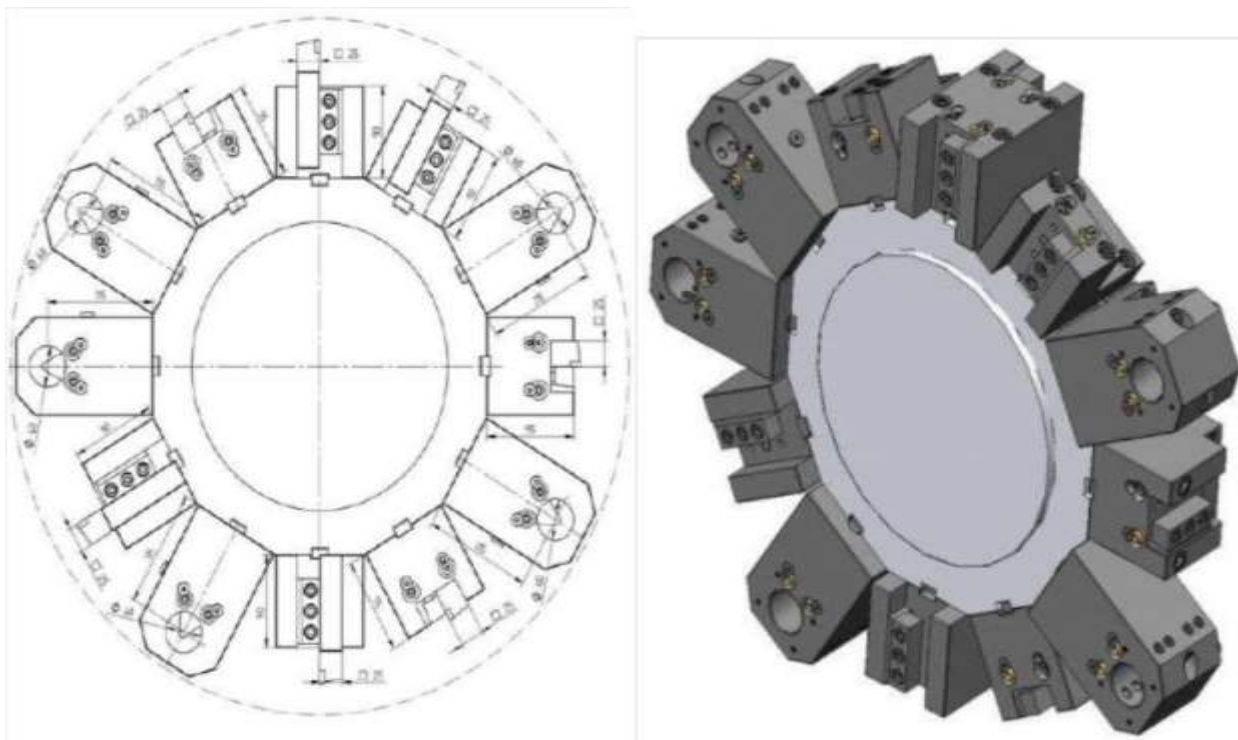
Револьверна головка ВМТ з державками без приводного інструмента[3]
